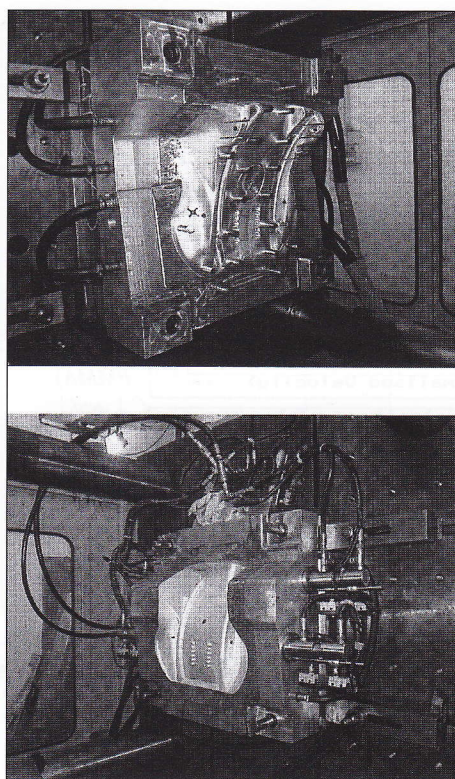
Stampi in lega di alluminio per injection-molding.
